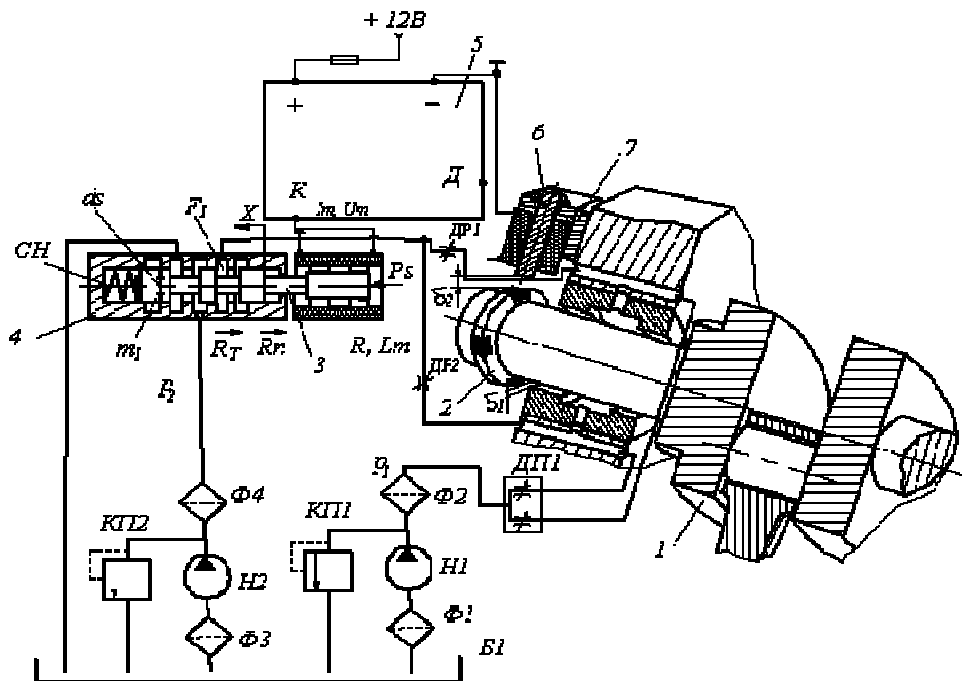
Функциональная схема электрогидравлической САУ: 1 – коленчатый вал; 2 – кольцо с ферромагнитными вставками; 3 – плунжер; 4 – корпус золотника; 5 – фазочувствительный усилитель напряжения; 6 – датчик магнитоэлектрический; 7 – корпус датчика
